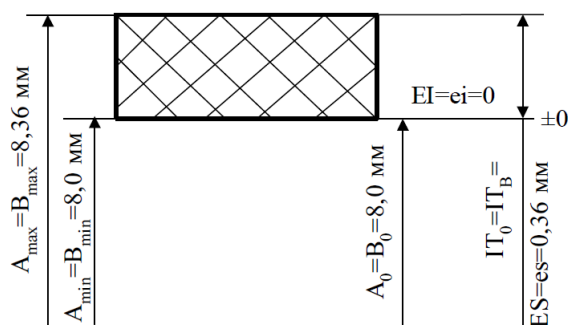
Схема расположения полей допусков отверстия и вала
